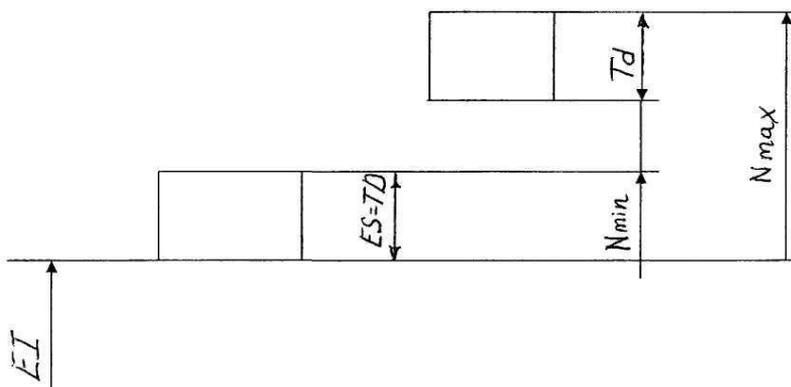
Схема расположения полей допусков деталей соединения.
